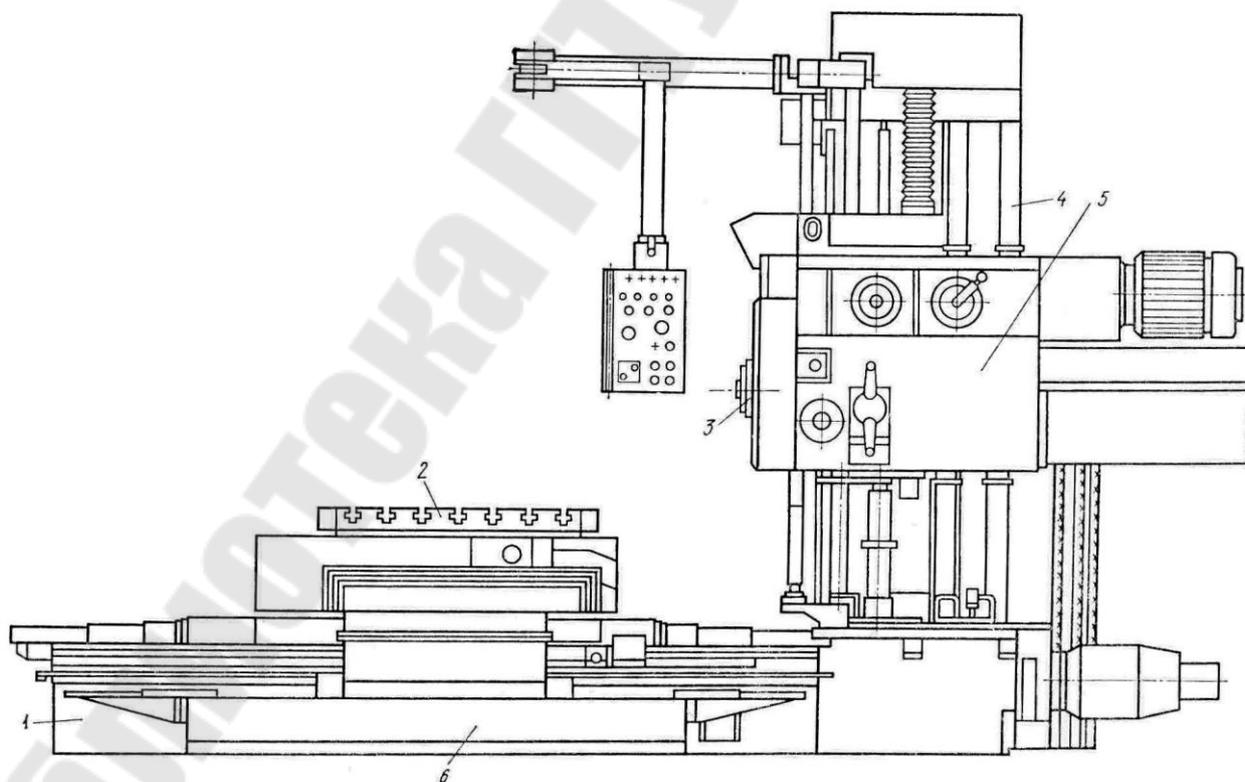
Общий вид станка модели 2А622Ф4
